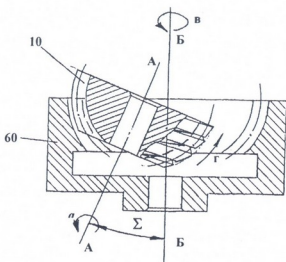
Схема нарезания некруглого цилиндрического колеса с внутренними зубьями
